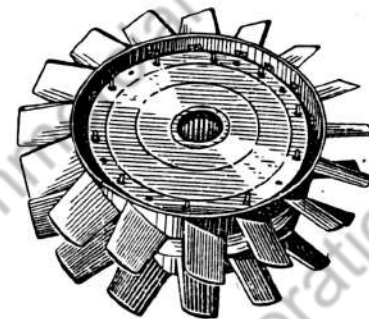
Вентилятор (вид со стороны ведущего диска).
